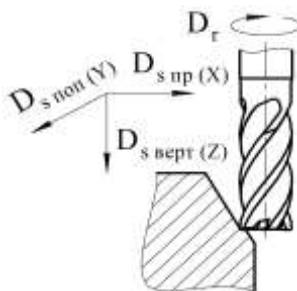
Формообразующие движения вертикально-фрезерного станка
